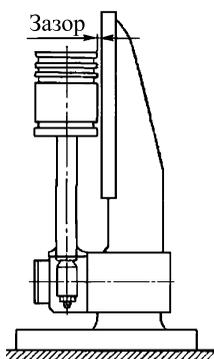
Схема приспособления для контроля сборки шатуна с поршнем
